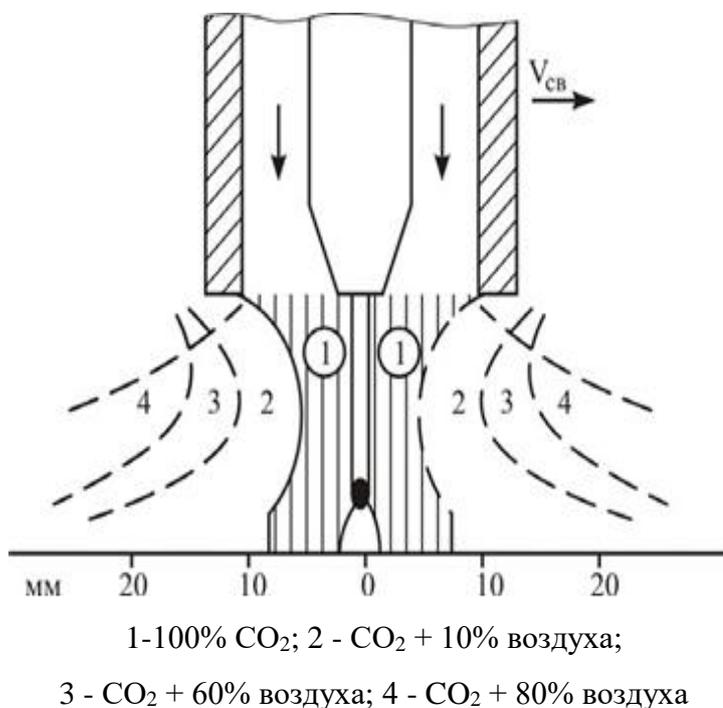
Компонентный состав потока углекислого газа, выходящего из сопла сварочной горелки
